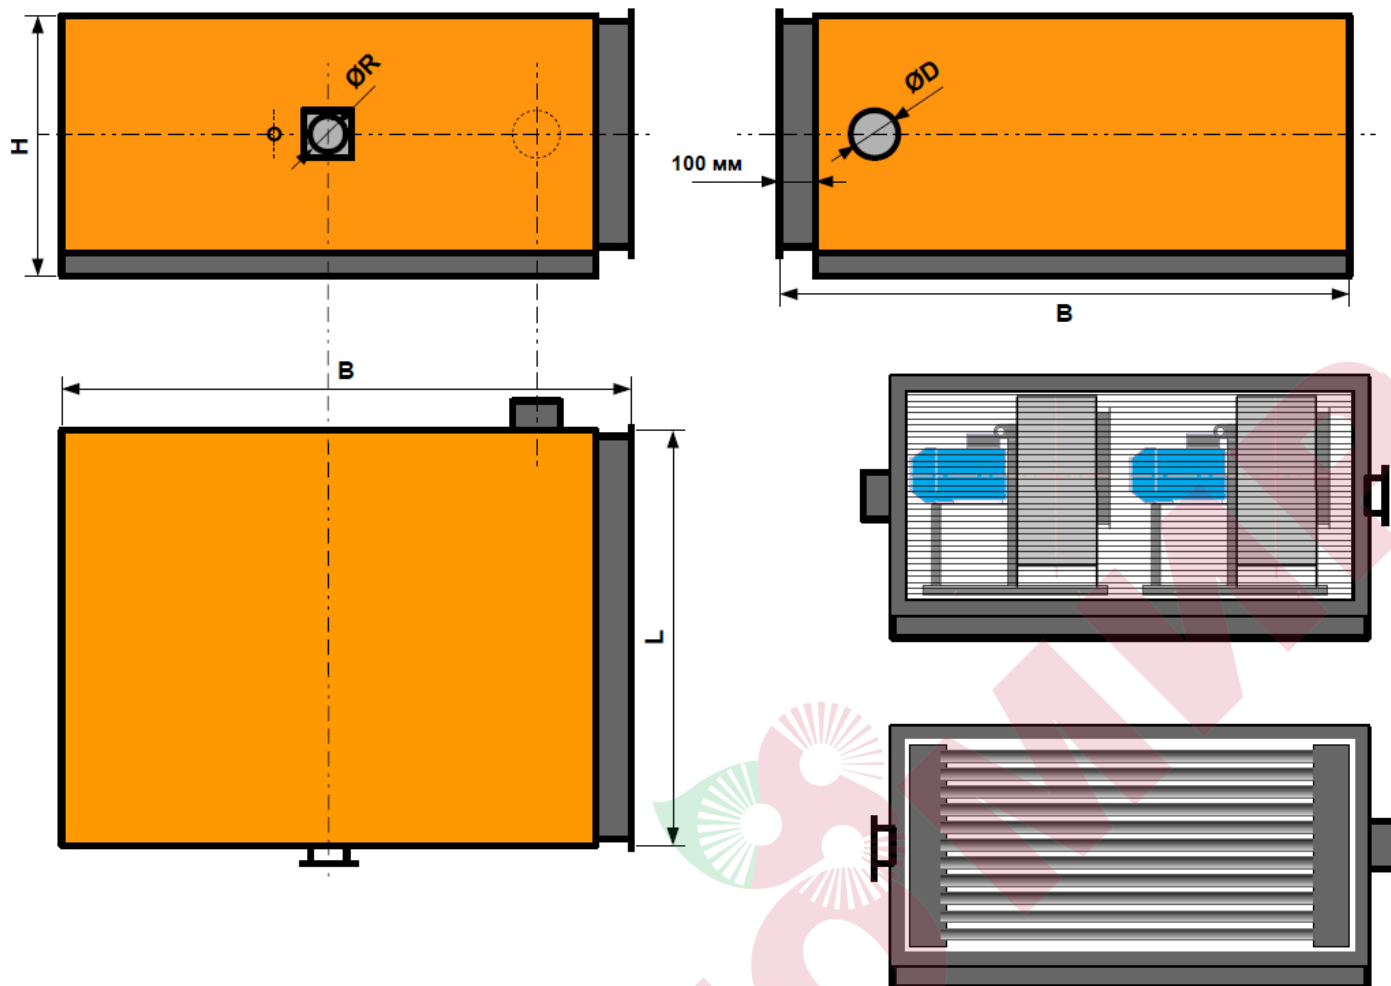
Габаритные размеры воздухонагревателей серий НТ-К
